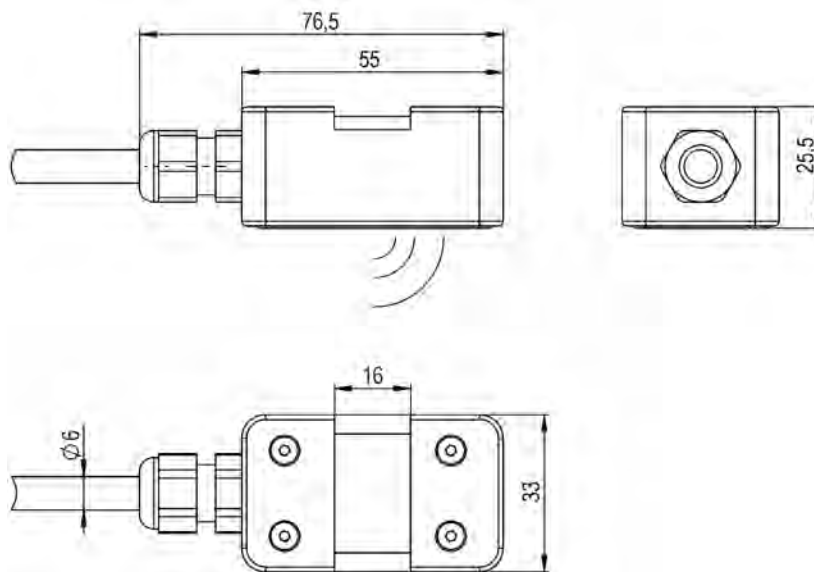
Maßzeichnung Clamp-On Sensor Typ NIC-CO01
